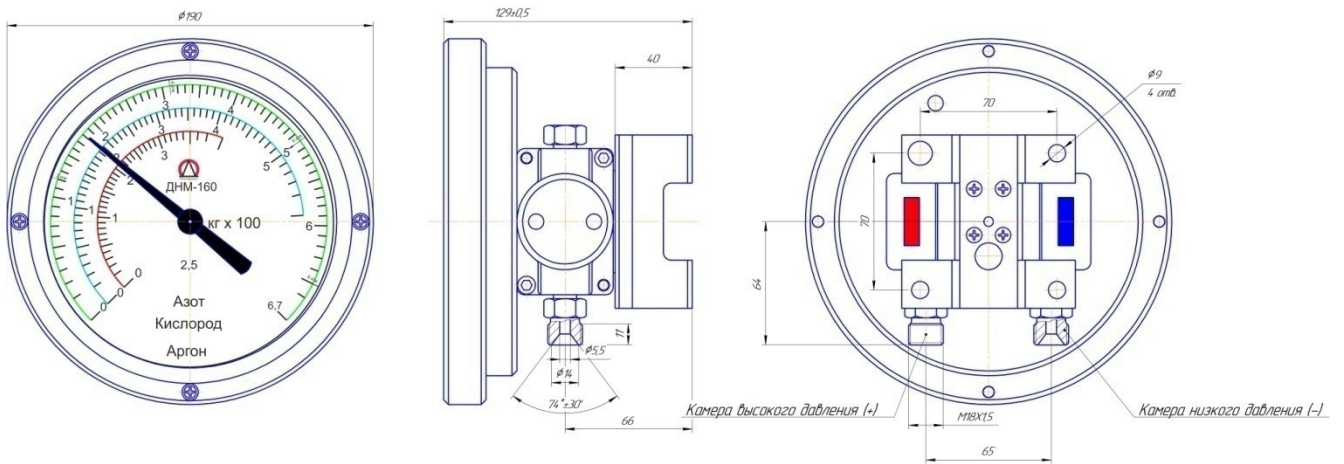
Габаритные и присоединительные размеры Дифманометра- уровнемера ДНМ-160
